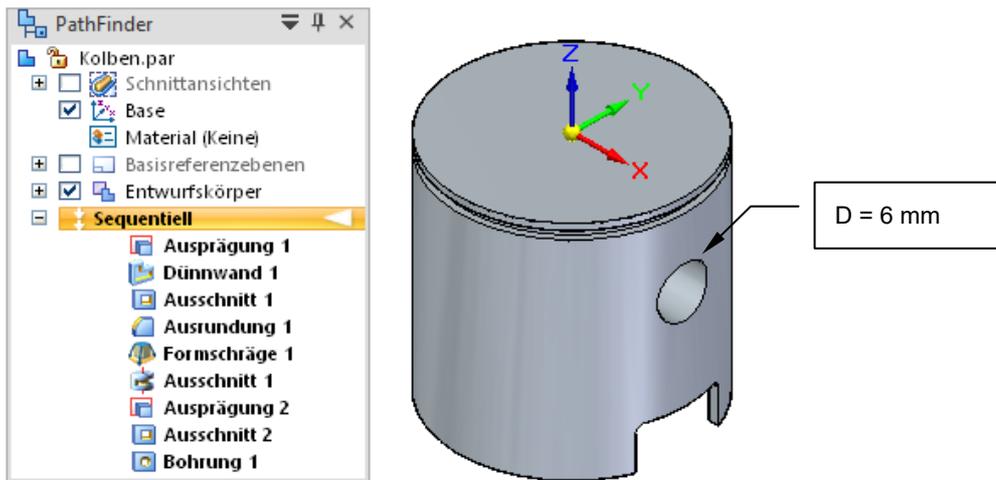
Die Bohrung für den Kolbenbolzen
